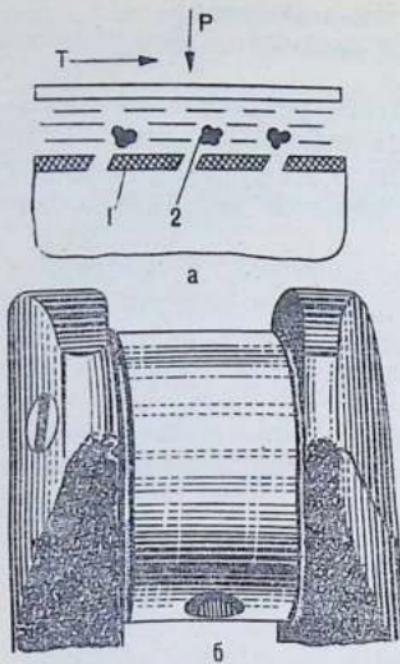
Схема разрушения поверхности детали от окислительного изнашивания и внешний вид детали, претерпевшей окислительное изнашивание:
